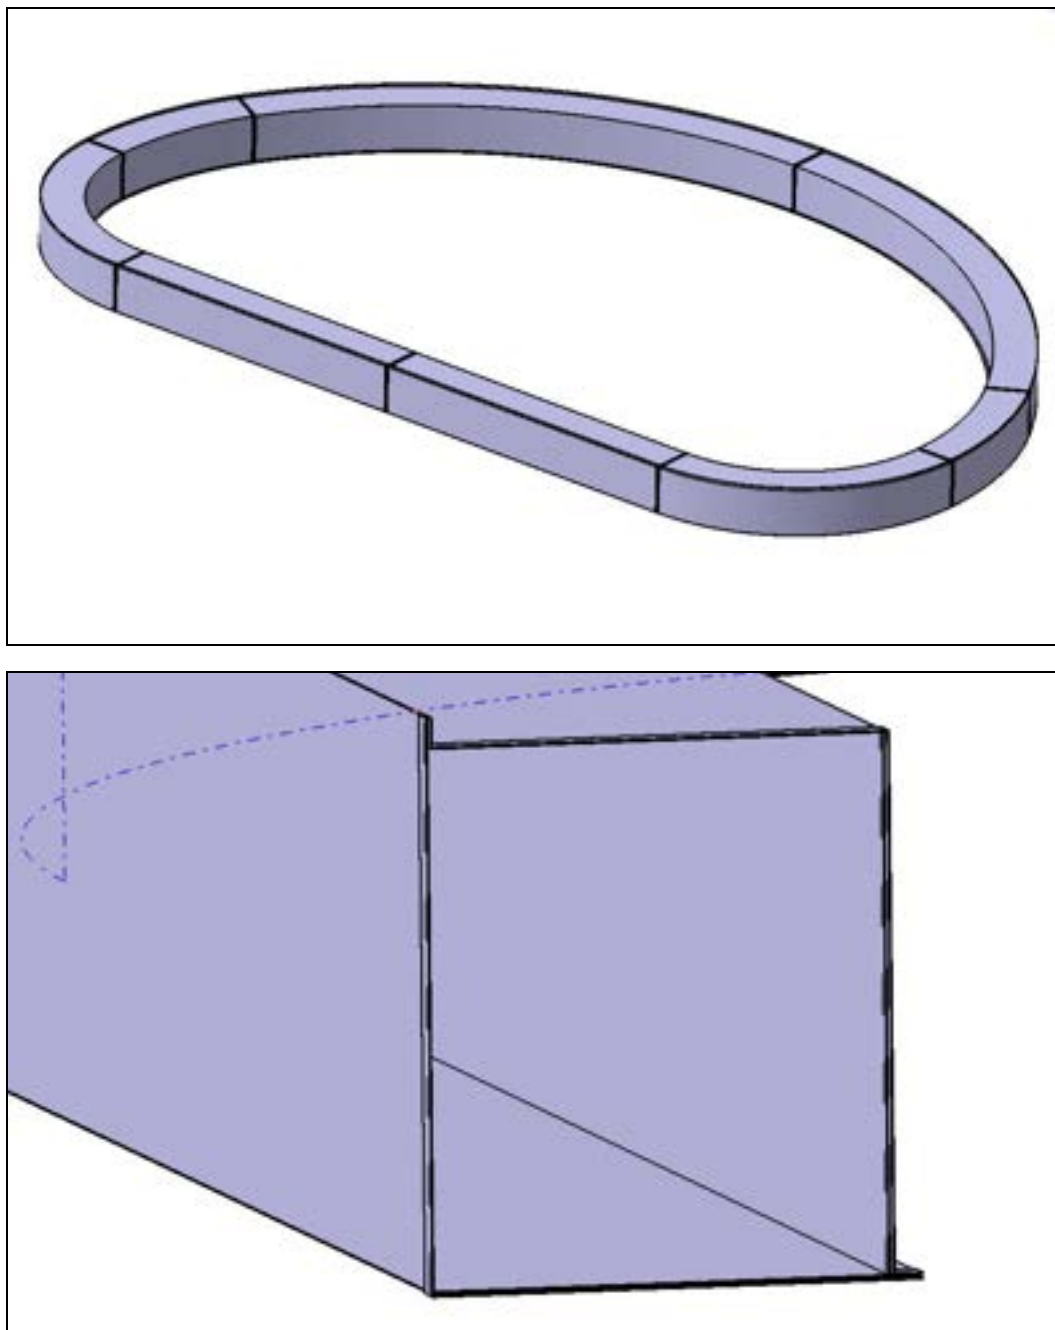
/3b: camera contenimento (sinistra) e dettaglio sezione (destra)
